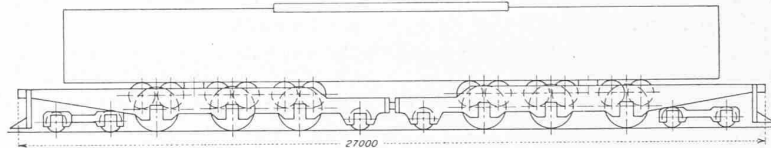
Schnellzuglokomotive 2C1+1C2 der Westinghouse El. & Mfg. Co. für die Chicago Milwaukee & St. Paul Ry.
